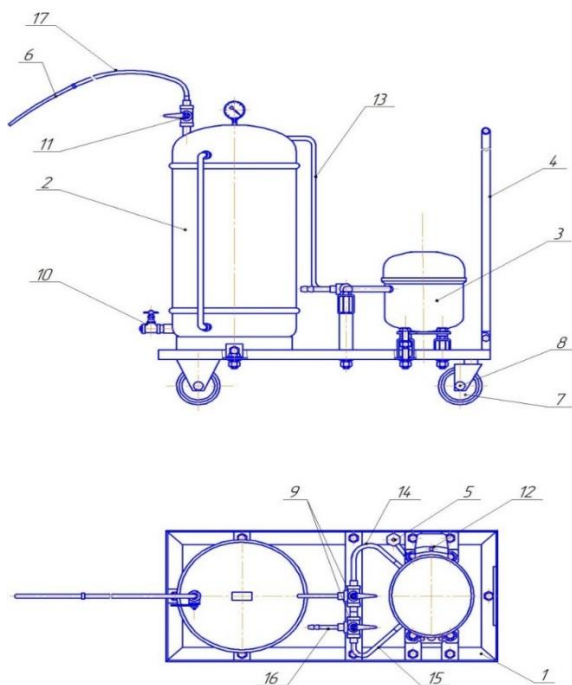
Разрабатываемая конструкция установки для сбора отработанного масла
